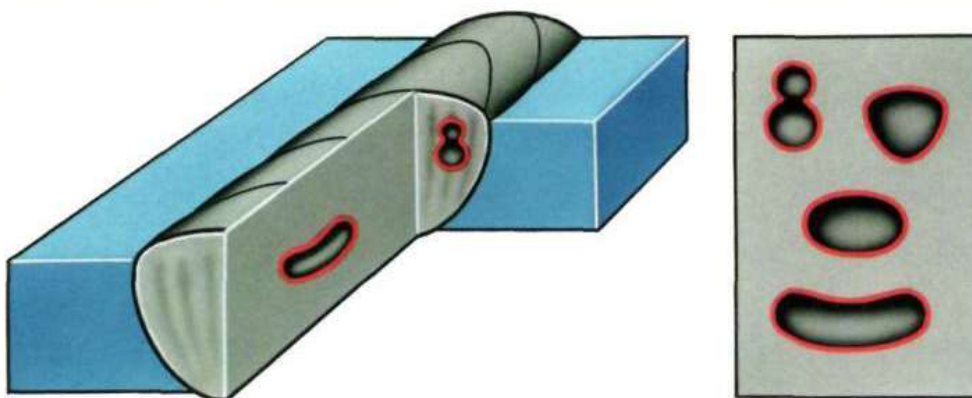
Дефекты сварного шва по типу газовой полости
